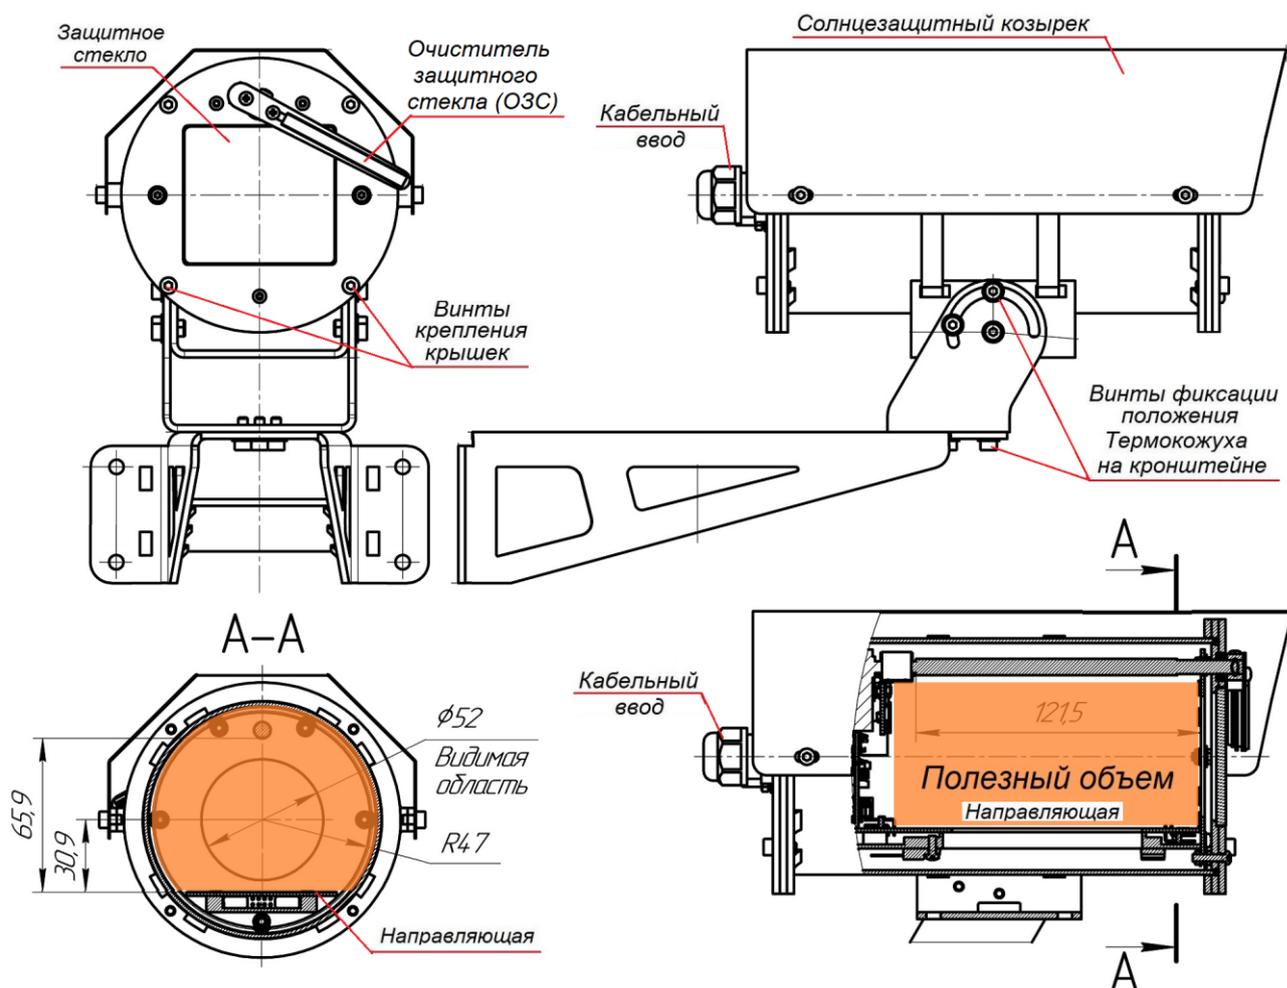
Внешний вид термокожуха BSM-180MV и назначение его конструктивных элементов
